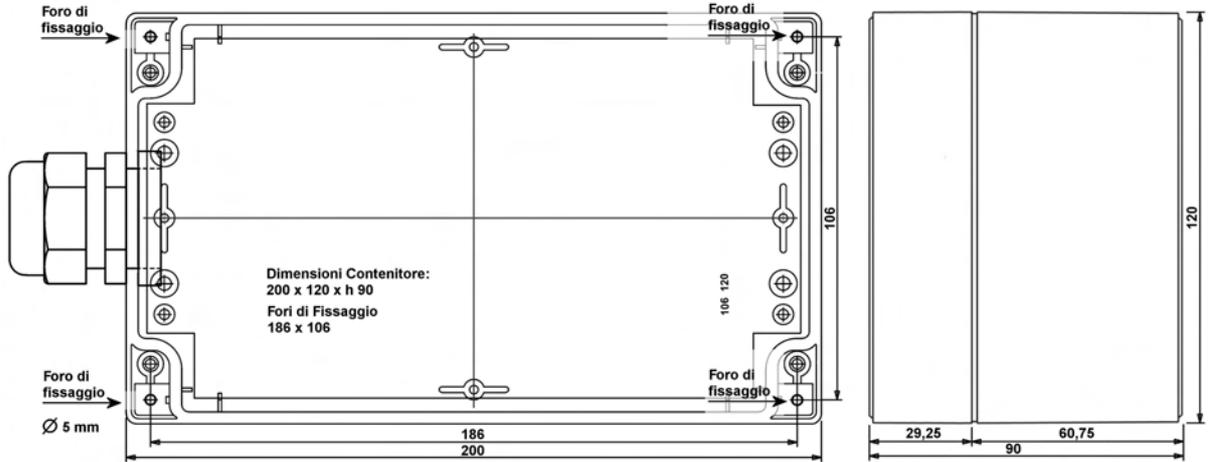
Ricevitore RSL : Dimensioni e fori di fissaggio
